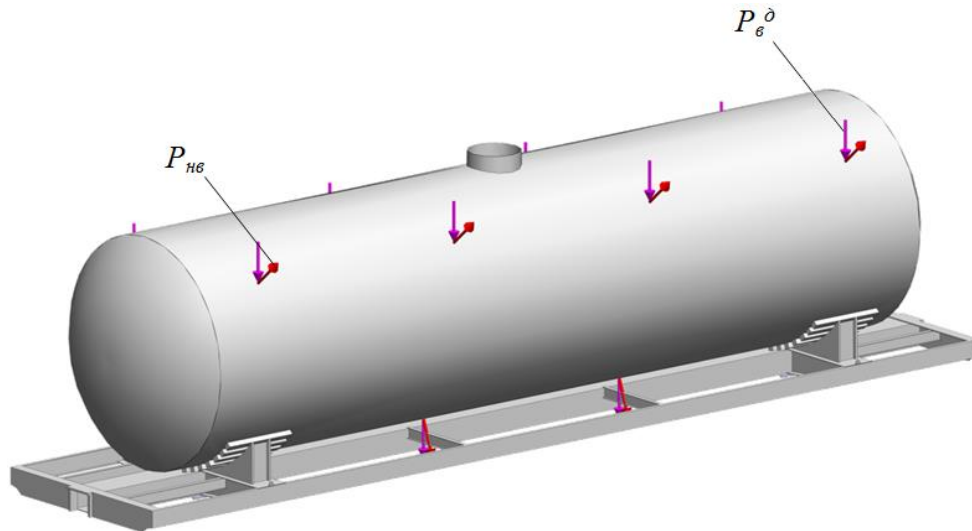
Розрахункова схема несучої конструкції вагона-цистерни
